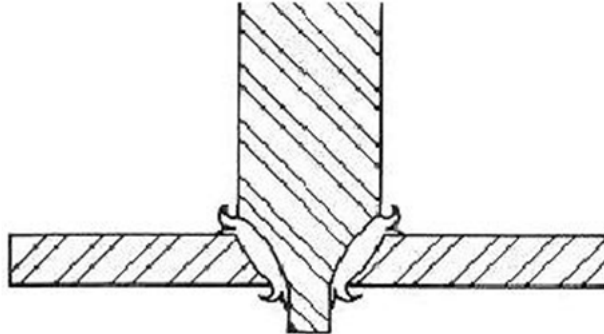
Junta angular para soldagem tipo *Friction Stitch Taper*<sup>(3)</sup>.
